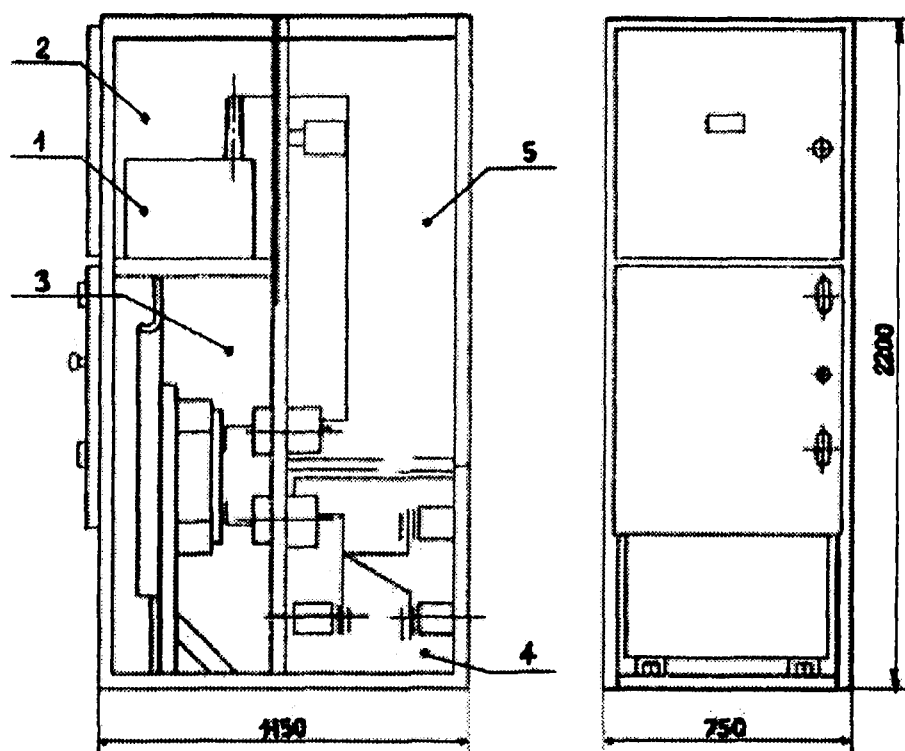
Общий вид и габаритные размеры шкафа серии К-104М с конденсаторами
